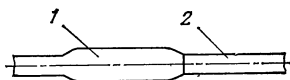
Схема соединителя электрода старой конструкции фирмы «Тесла»:
